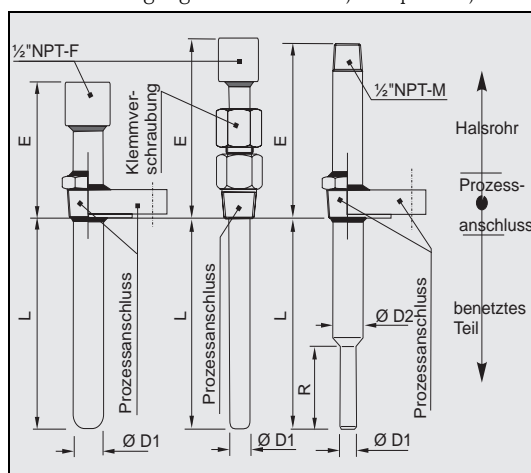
Schutzrohr mit Gewinde- oder Flanschprozessanschluss
